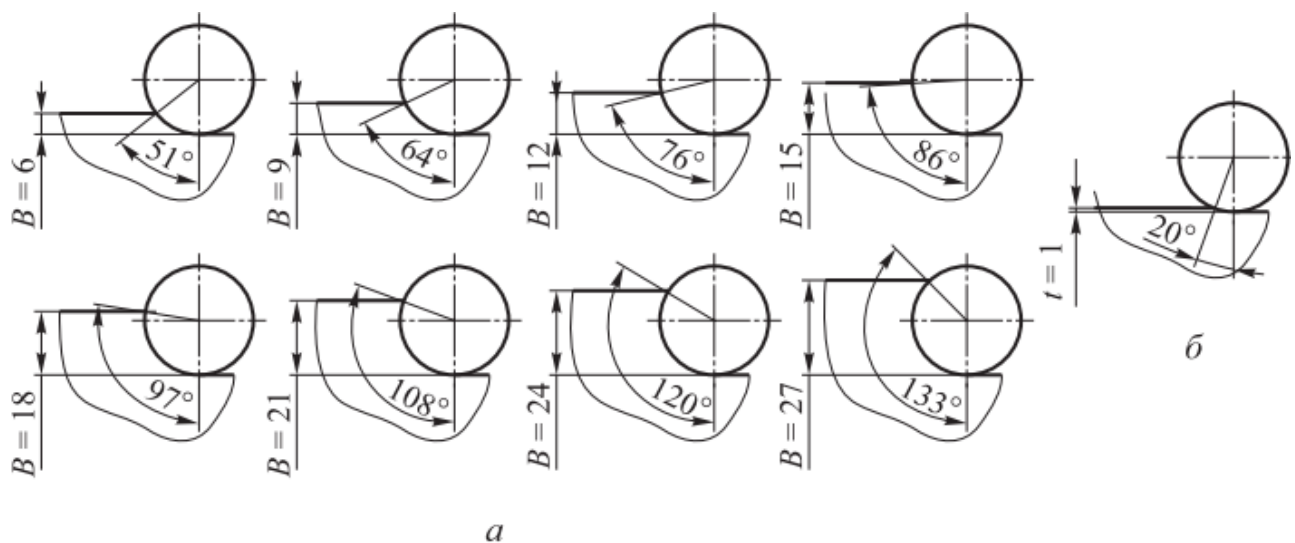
Геометричне визначення зношення кутів контакту зуба для торцьового (а) й циліндричного (б) фрезерування
